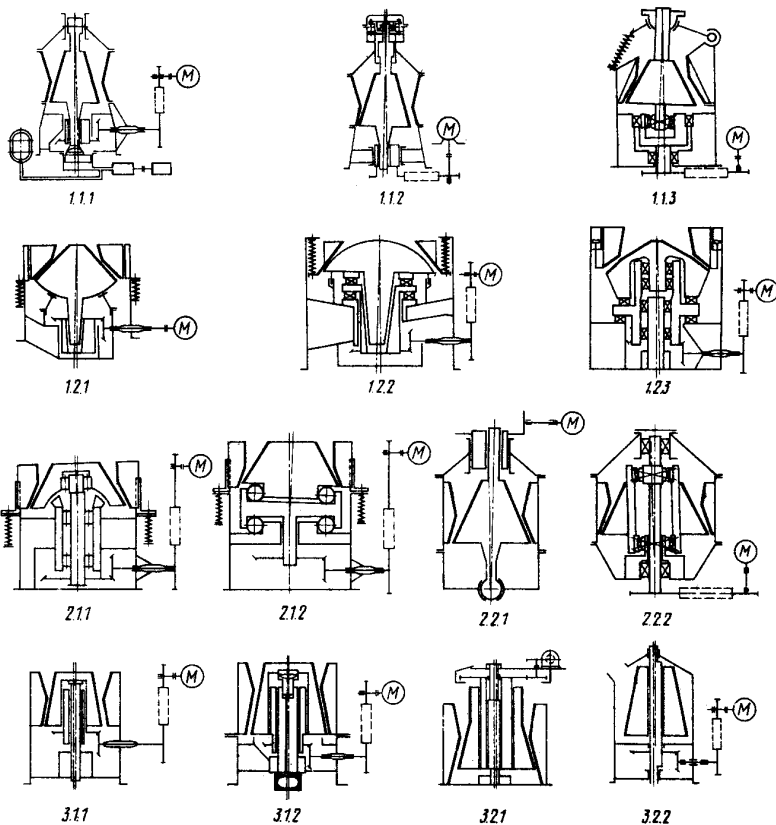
Конструктивные схемы дробилок: 1.1.1 – 1.2.3 — с точкой подвеса над камерой; 2.1.1 – 2.2.2 — с нижним расположением точки гирации; 3.1.1 – 3.2.2 — с параллельными осями дробилки и подвижного конуса.
